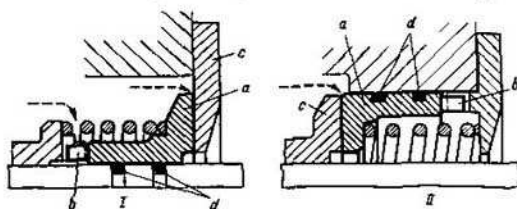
Esquema de una empaquetadura frontal. El disco de empaquetadura está fijado:
